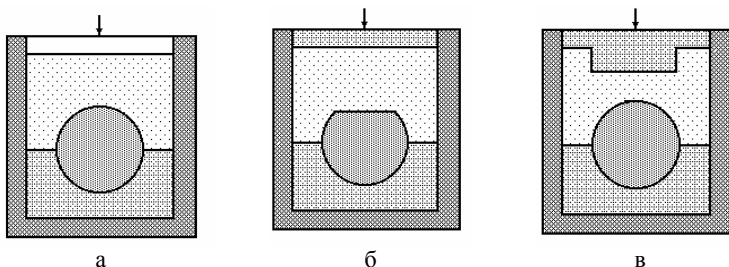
Схемы радиального СВС-прессования цилиндров:
